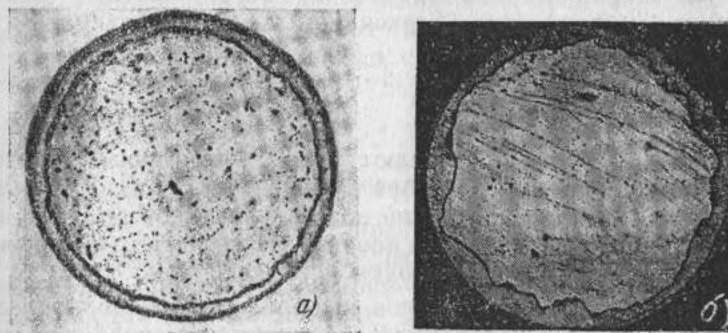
Поперечный разрез платинитовой проволоки.
